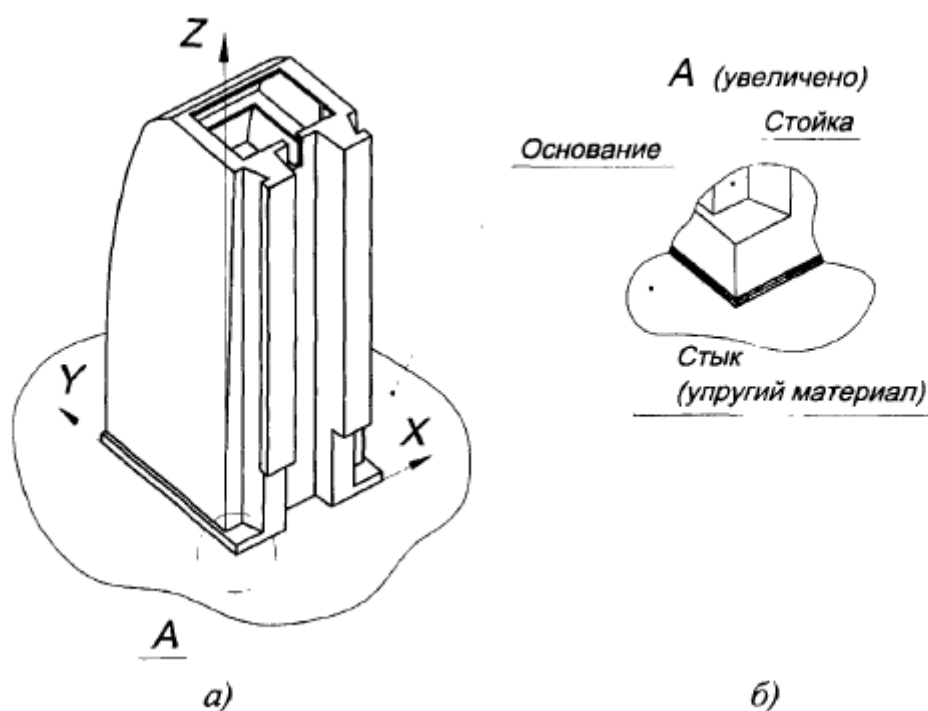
а) Стойка фрезерного станка мод 654 б) Схема стыка
